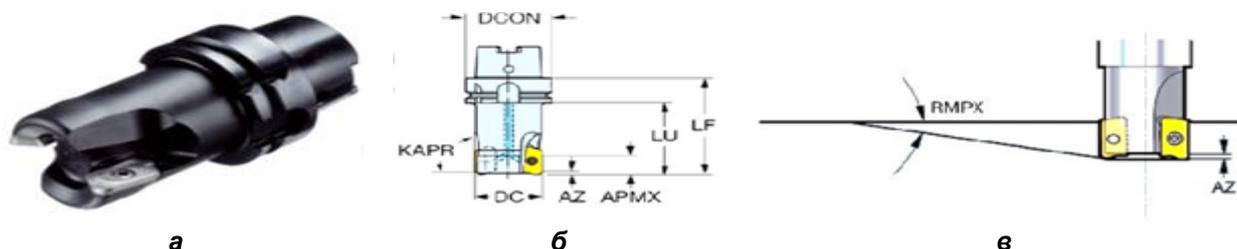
Фреза для обработки уступов R790-025HA06S2-16L:
